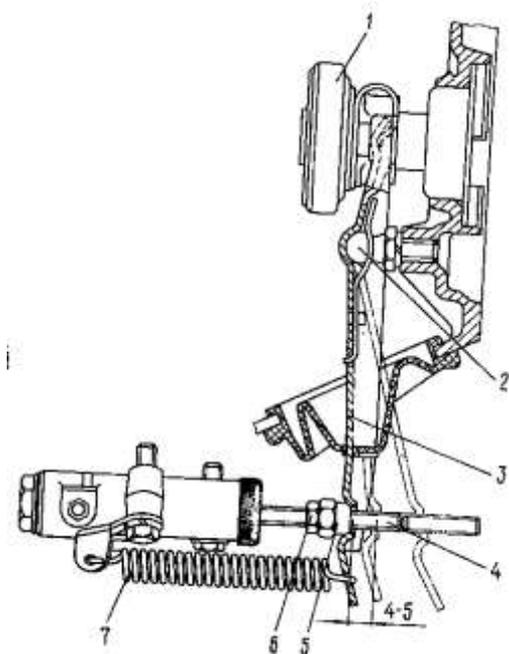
Рабочий цилиндр и вилка выключения сцепления:
